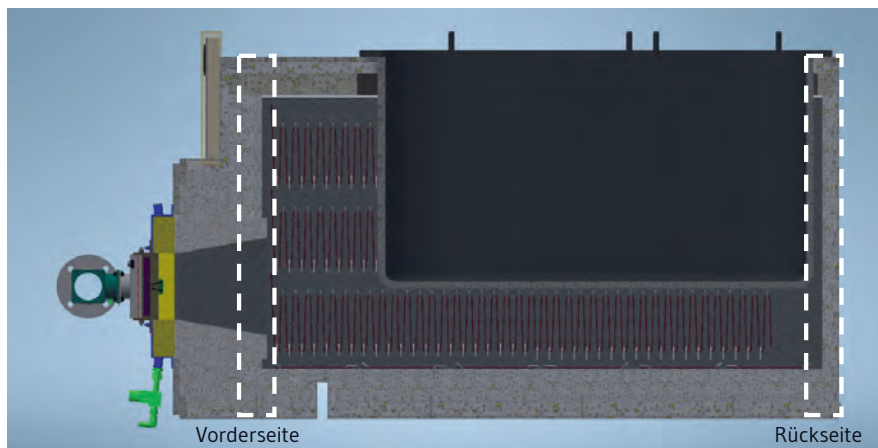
Schnitt des ausgearbeiteten Ofenkonzepts mit Oberflächenbrenner
